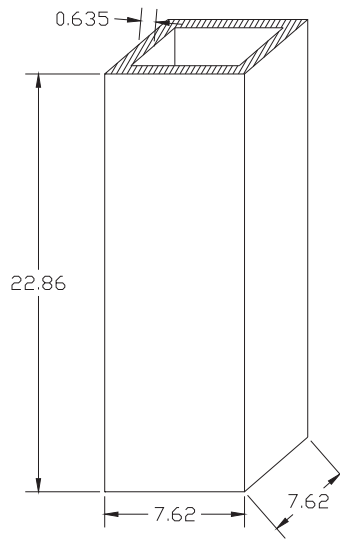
Geometría y Dimensiones del molde utilizado para la fabricación de los lingotes (cm).
